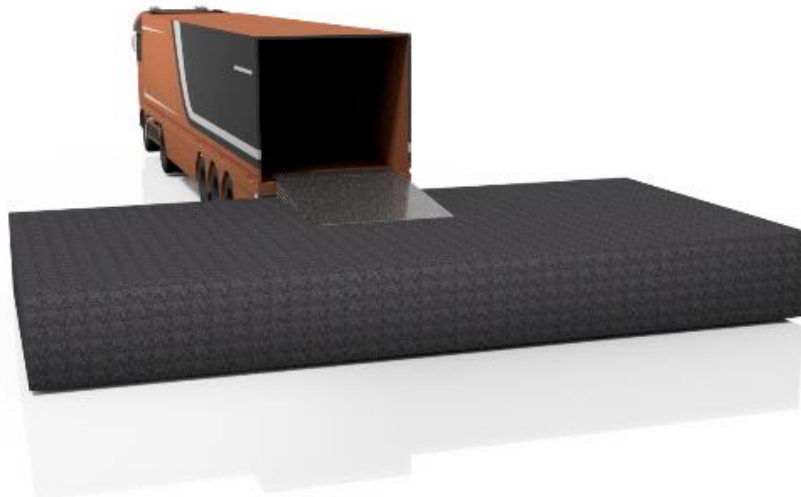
Nivelador de Cais em desenvolvimento; Render CAD
